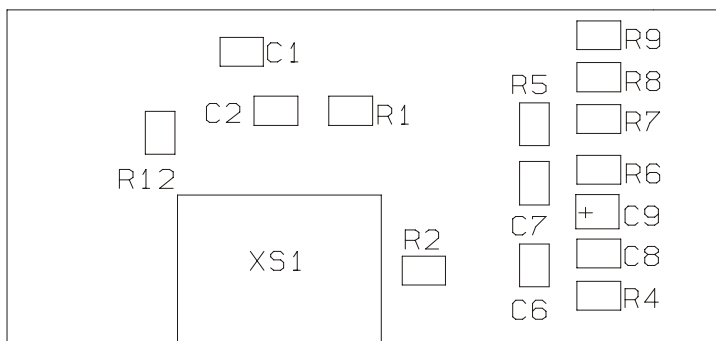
Сборочный чертеж платы обработки блока датчика СКГГ варианта исполнения 1. Сторона пайки.
